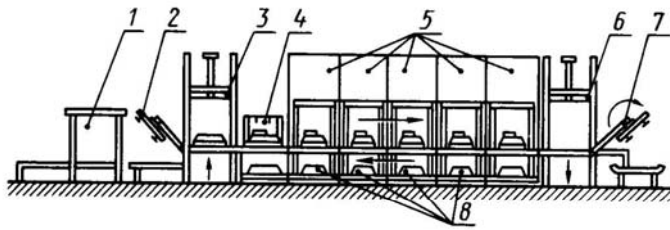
Схема автоматической линии сборки и сварки настила пола кабины грузового автомобиля ЗИЛ
